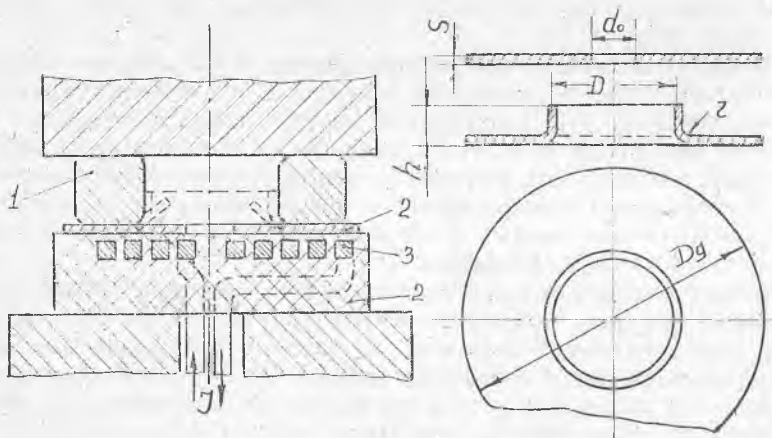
Схема процесса отбортовки отверстия с использованием энергии ИМП: 1—матрица, 2—заготовка, 3—спираль индуктора; 4—корпус индуктора
